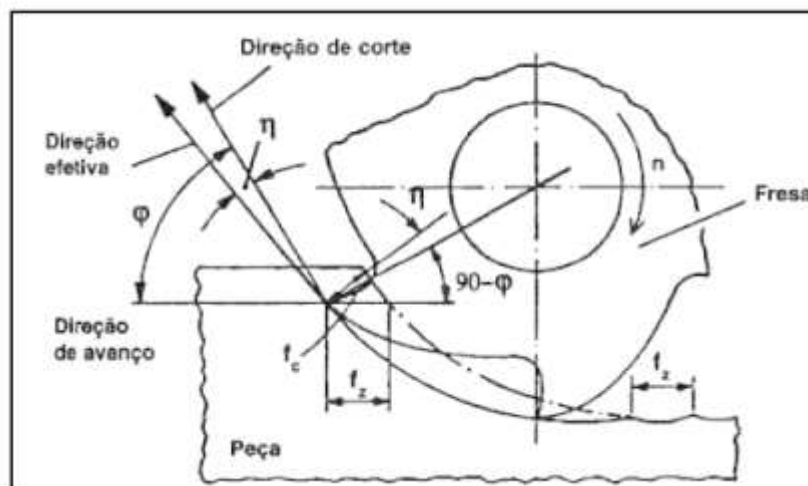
Avanço por dente (f_z), avanço de corte(f_c) no fresamento discordante. (NBR 6162, 1989).
